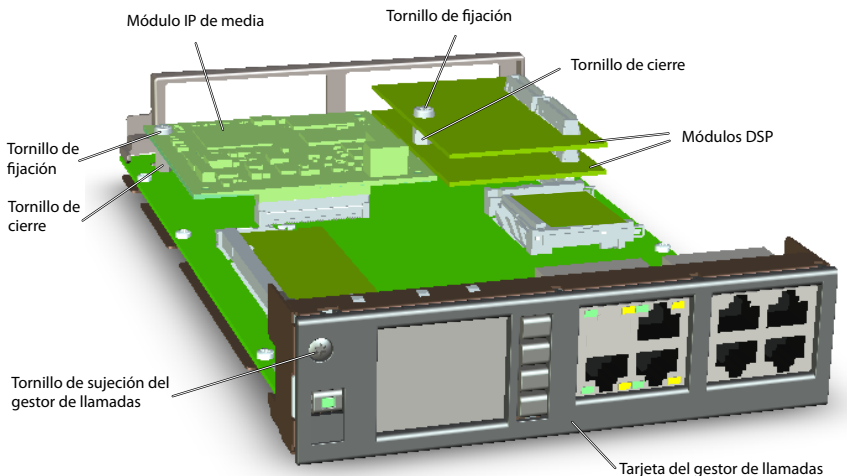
Módulos de sistema en la tarjeta gestor de llamadas
